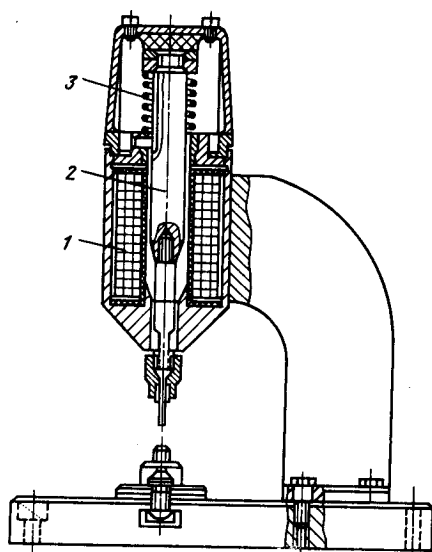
Электромагнитный пресс: 1 — обмотка; 2 — якорь; 3 — пружина
